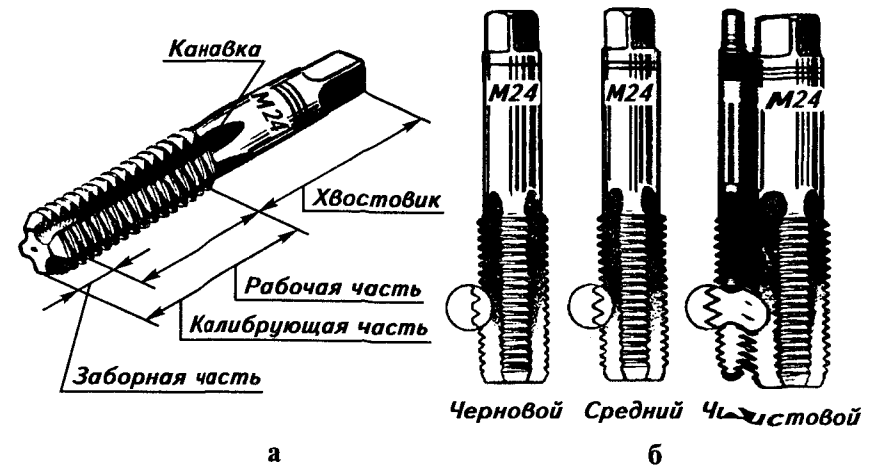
Метчики: а — устройство; б — комплект для нарезания метрической резьбы
